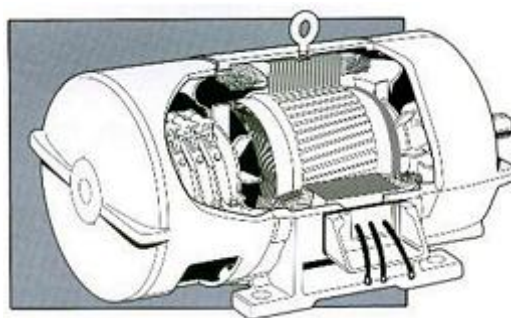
MADA à rotor bobiné (document "Joliet Equipement")
